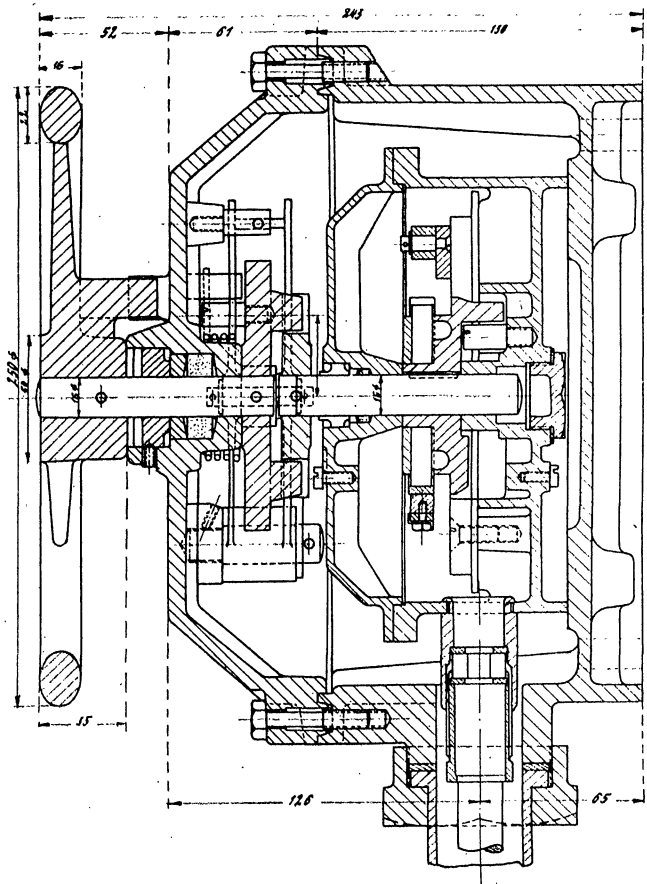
Druckwasserdichter Steuerschalter (Brücke) für Rudermaschinen mit unmittelbarer Fernsteuerung der Bergmann E. W.
